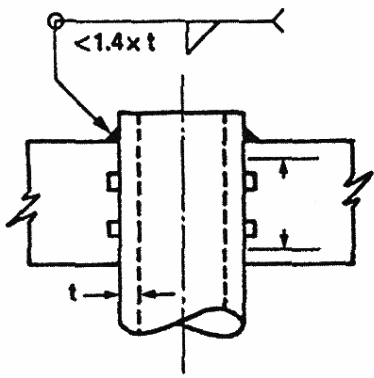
Развальцовка с герметизирующей сваркой.
